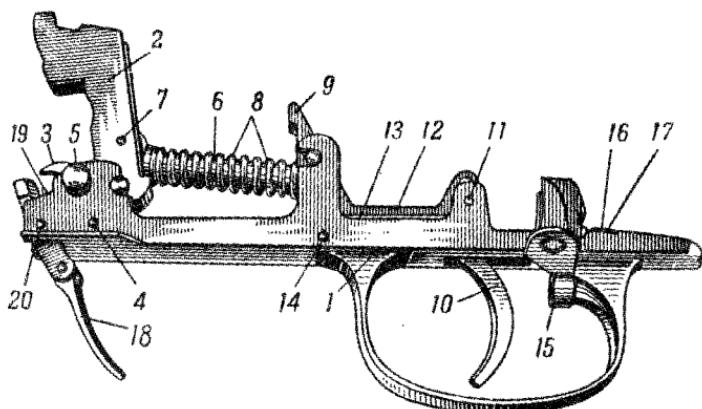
Ударно-спусковой механизм СВТ-40: 1 - спусковая скоба; 2 - курок; 3 - автоматический спуск; 4 - ось автоматического спуска; 5 - пружина автомата спуска; 6 - направляющий стержень; 7 - опорная шпилька; 8 - боевая пружина; 9 - коромысло; 10 - спусковой крючок; 11 - ось спускового крючка; 12 - спусковая тяга; 13 - пружина спусковой тяги; 14 - шпилька пружины; 15 - предохранитель; 16 - пружина и стопор предохранителя; 17 - задвижка; 18 - защелка магазина; 19 - пружина защелки; 20 - ось защелки.
